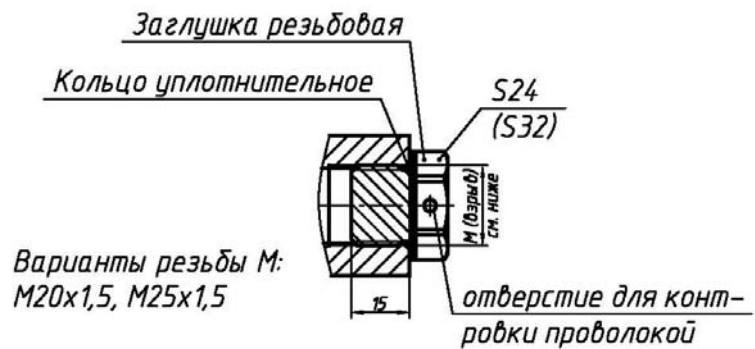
Элементы взрывозащиты при поставке извещателя с резьбовыми заглушками (условное обозначение З).
